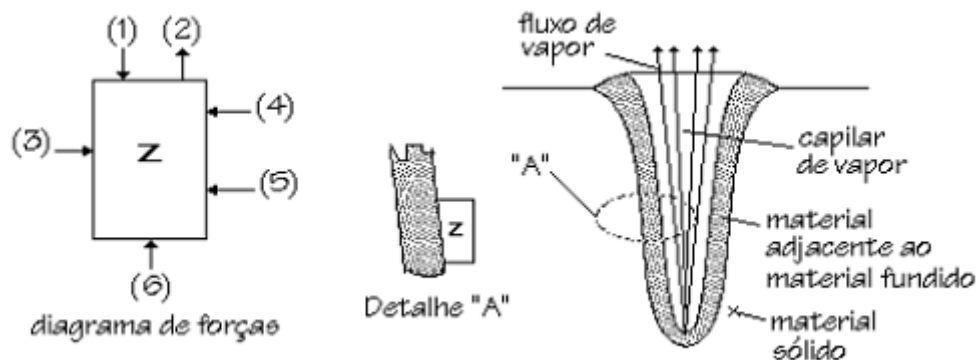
Forças presentes durante a soldagem com a técnica do key-hole
